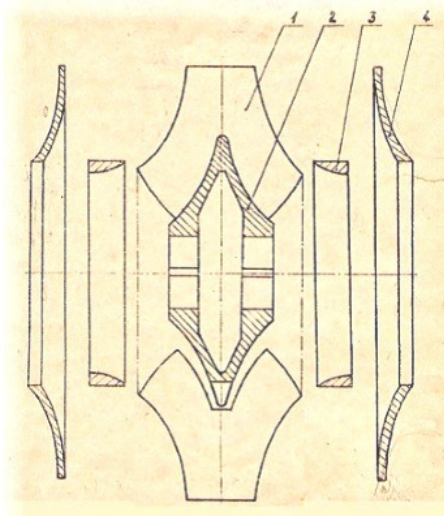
Составные части рабочего колеса сварной конструкции центробежного насоса 24НДс
